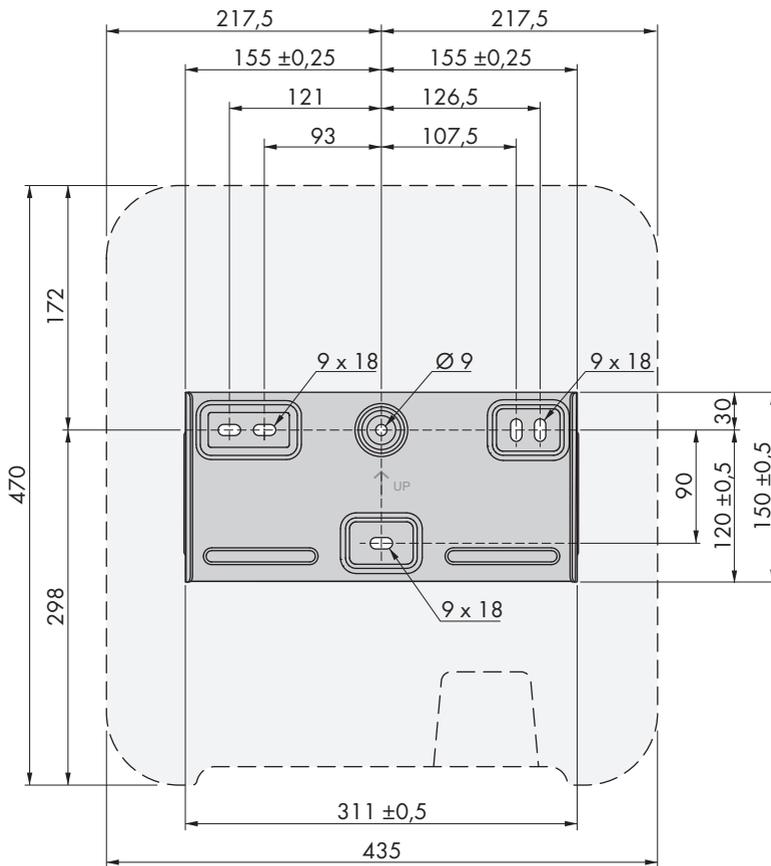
Posição dos pontos de fixação (dimensões em mm)
